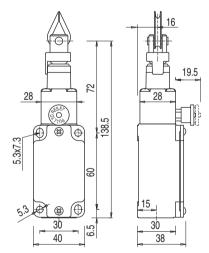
Dimensions de l'ERS200-MxC1x-HLR en mm
